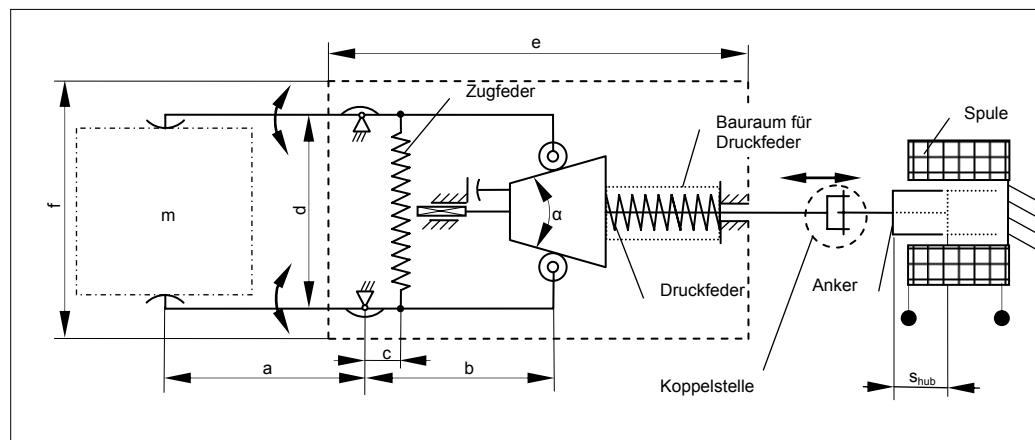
Greifer in Position „ZU“, (Draufsicht)
